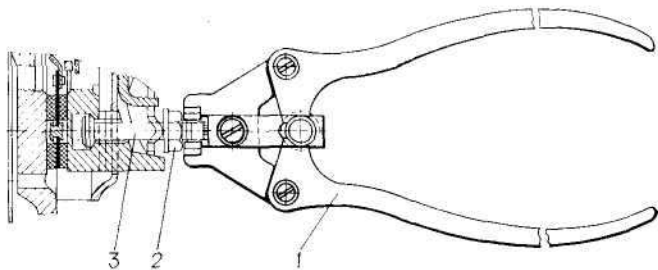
Клеши для фиксации регулировочных гаек, пальцев сцепления;
